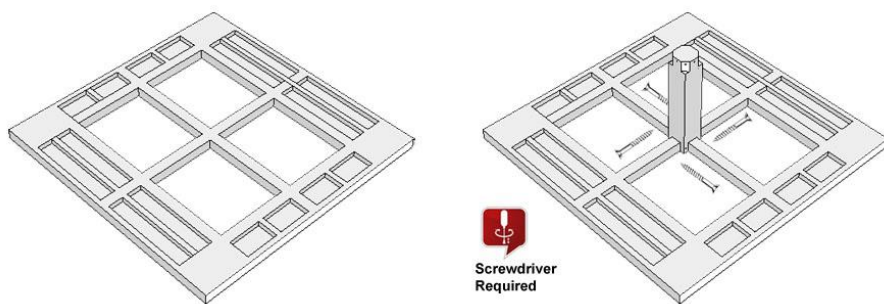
Parte inferiore del tetto e trave di supporto centrale
